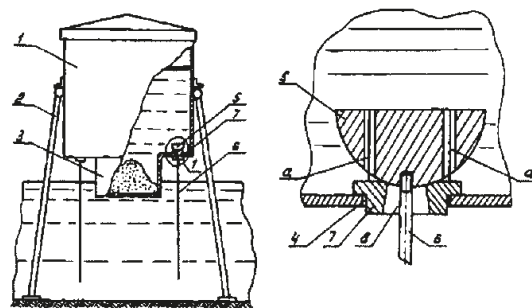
Устройство для выдачи извести маятниковым устройством. 1- бункер; 2- опоры; 3-приемник для извести; 4- резиновая прокладка; 5- полусфера; 6- маятник; 7- шайба; 8-отверстие.
